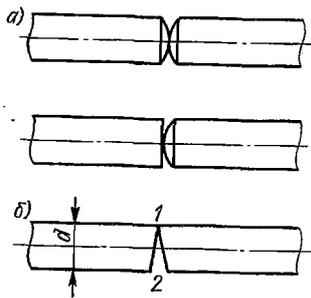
Конструктивная подготовка деталей для стыковой сварки
